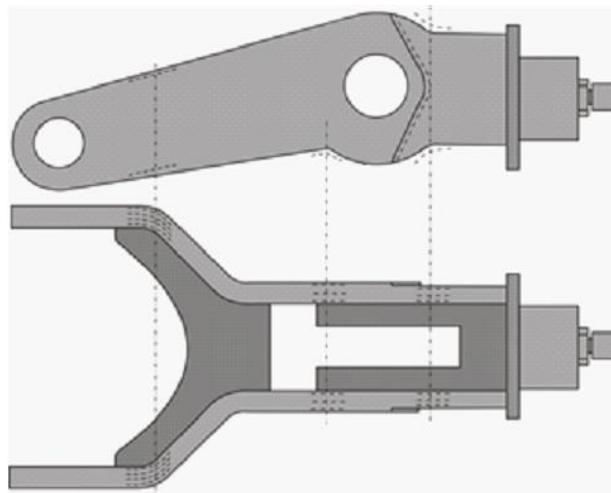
Схема сканирования околошовных зон сварных соединений деталей рычага рычагов 4075.42.130 и 4075.42.130.1 клещевого механизма
